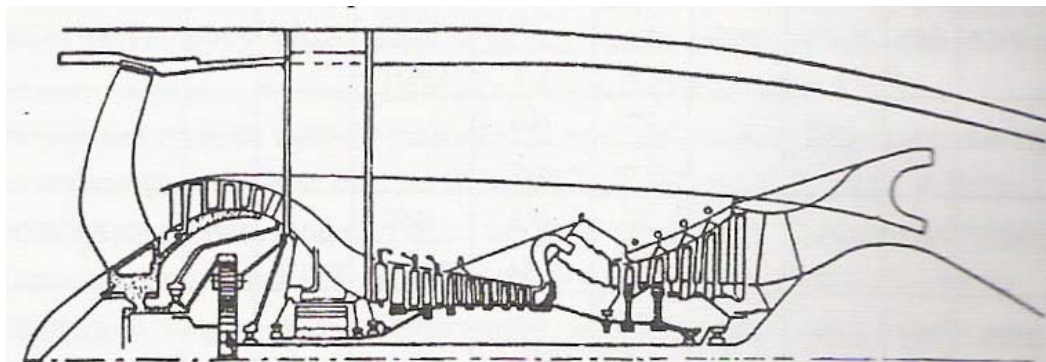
Схема двухконтурного двухвального турбореактивного двигателя с приводом вентилятора и компрессора низкого давления через редуктор от вала осевого компрессора высокого давления
